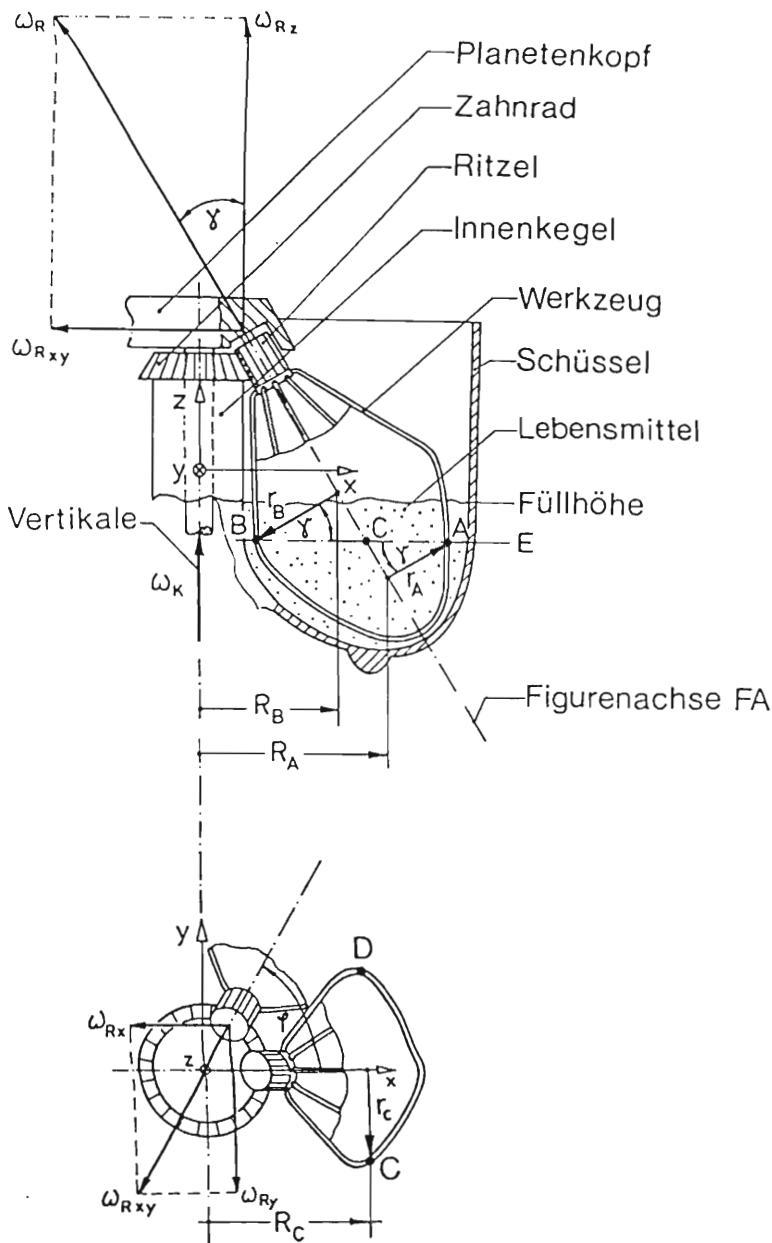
/16: Werkzeug und Planetenkopf sowie Schüssel mit Innenkegel einer Stand-Küchenmaschine klassischer Bauart
